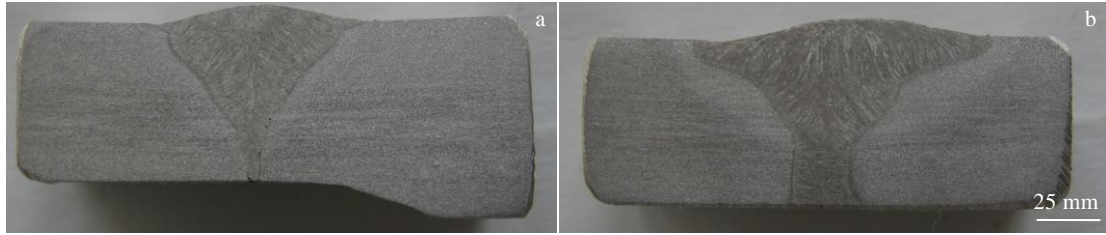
2 种保护气体下焊接接头宏观形貌
